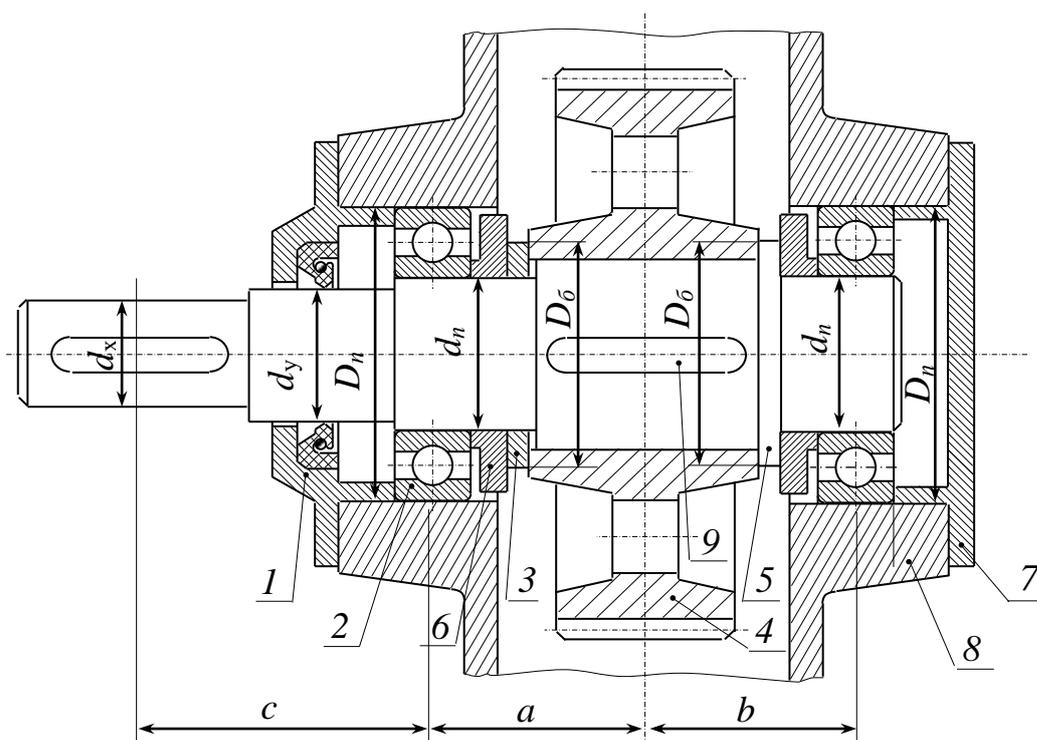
Узел вала колеса цилиндрического одноступенчатого редуктора: 1 – сквозная крышка подшипника; 2 – подшипник качения; 3 – дистанционное кольцо; 4 – зубчатое колесо; 5 – вал колеса; 6 – мазеудерживающее кольцо; 7 – глухая крышка подшипника; 8 – корпус редуктора; 9 – шпонка
